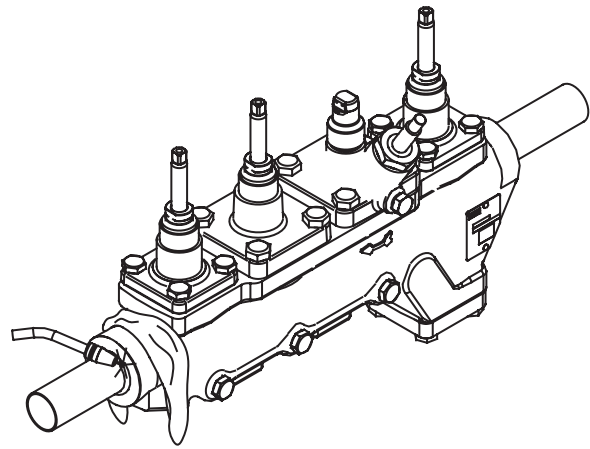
Soldadura con un Trapo Húmedo.
